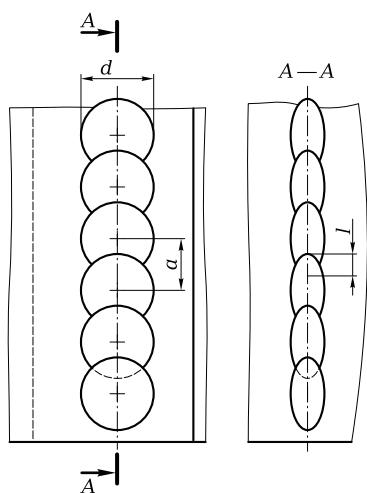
Конструктивные элементы соединений, выполненных контактной шовной сваркой:
